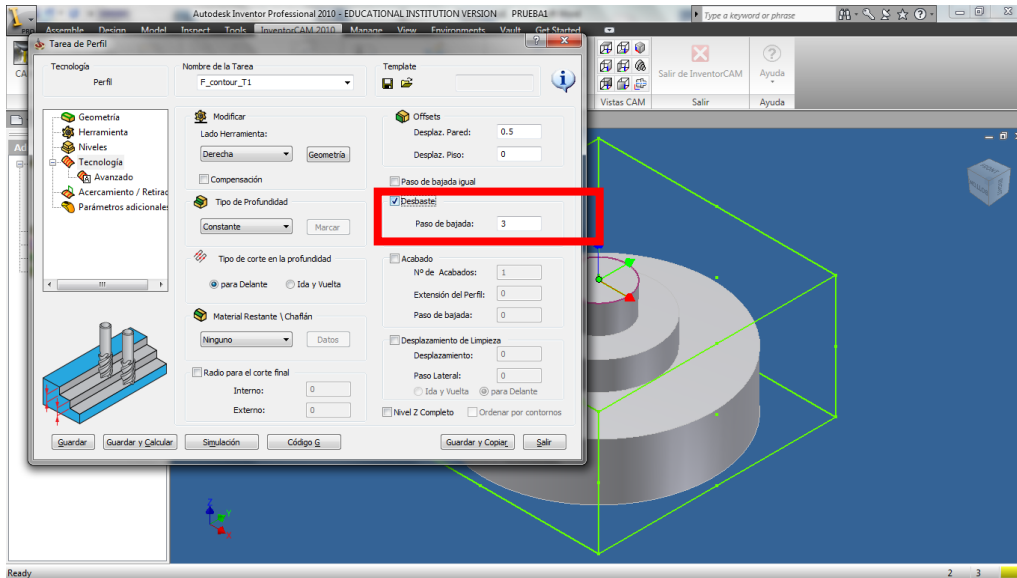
Maquinado Fresadora CNC – Definir longitud de desbaste
